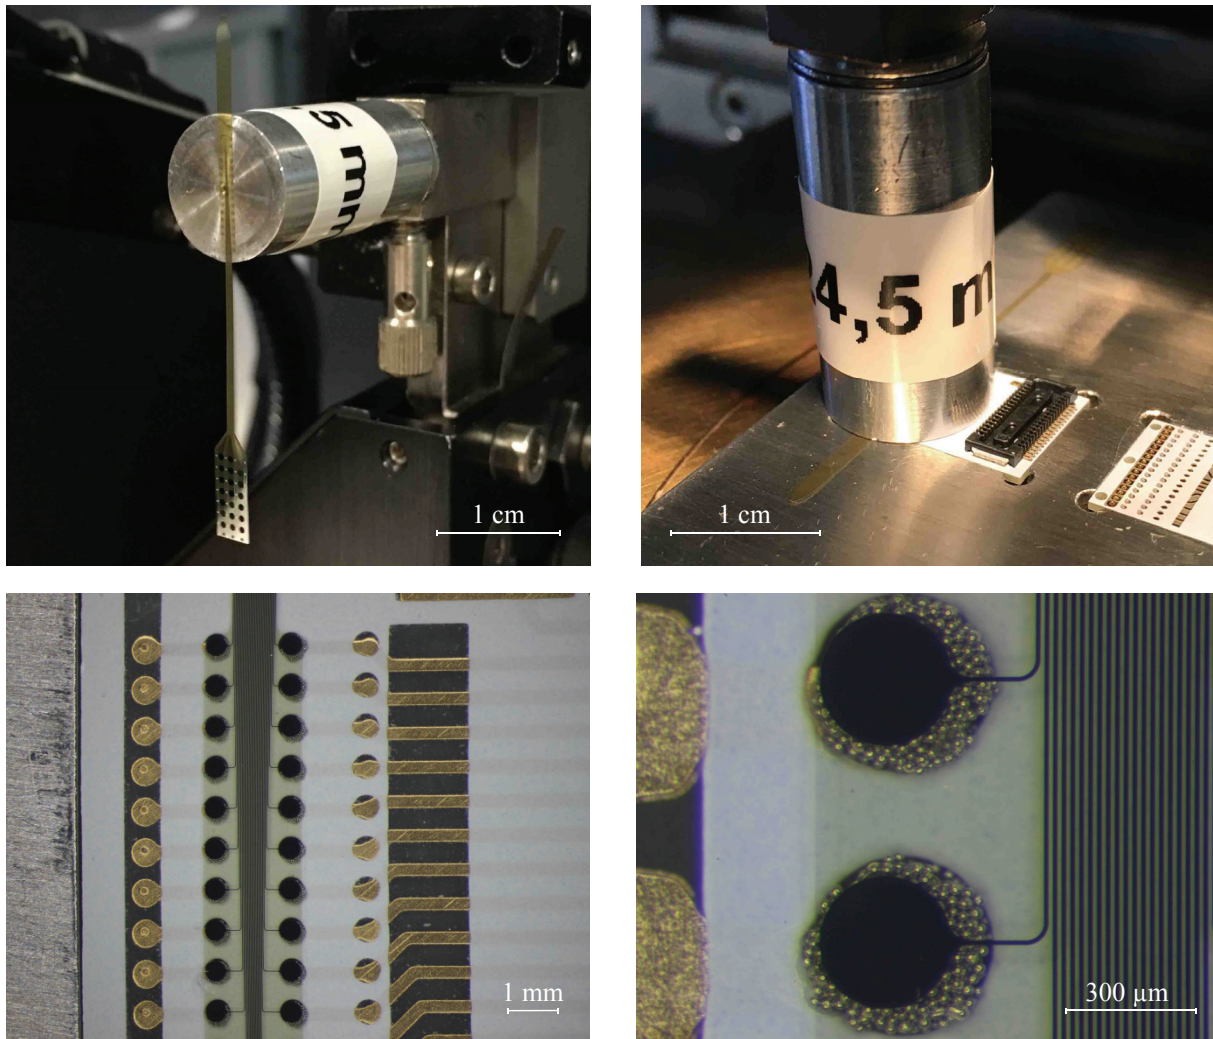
Vakuum unterstütztes “Pick and Place“ des ECoG-MEAs auf der Leiterplatte. Oben – Vakuumstempel in Ausrichtungposition mit angesaugtem Elektrodenarray (links) und Stempel unten zur Elektrodensubstratplatzierung auf PCB (rechts), Unten – Nahaufnahme des in der Lotpaste platzierten ECoG-MEAs (links) und detaillierte Ansicht (rechts)
